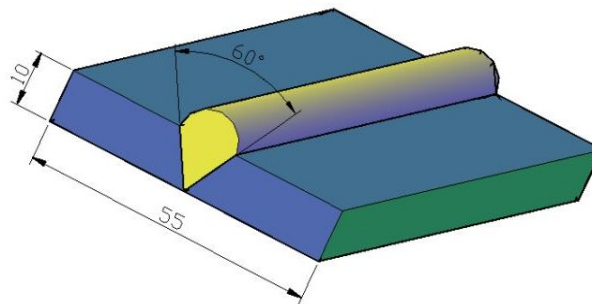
Lámina soldada en. (Fuente propia).
